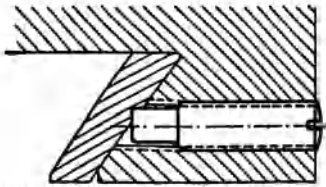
Anwendung des Gewindefestes mit Zapfen.
